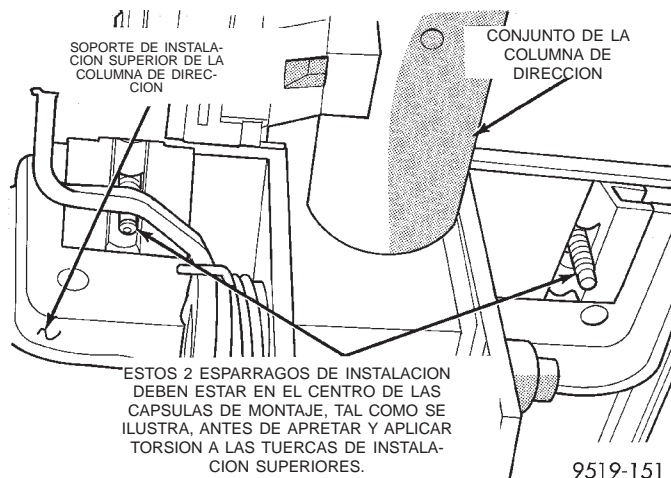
Tuercas del soporte de instalación superior e inferior de la columna de dirección
